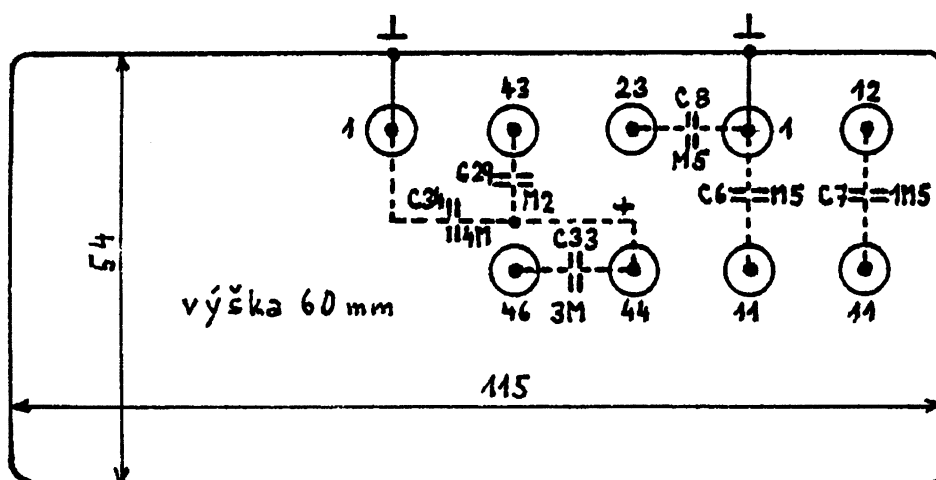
Zapojení součástek a vedení spojů pod šasi
